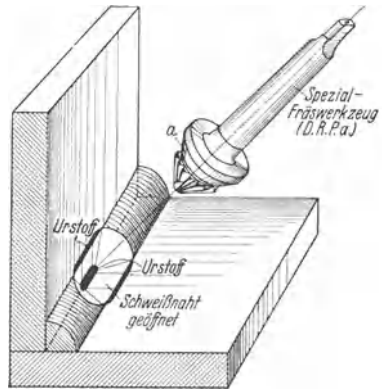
Prüfgerät für Schweißnähte nach Schmuckler.
